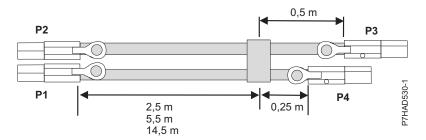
Comprimentos de cabo do conjunto de cabos externos SAS X
